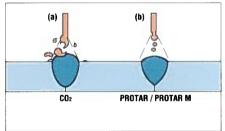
Efecto de la composición del gas sobre la transferencia del metal de aportación en la Soldadura MIG-MAG "Arco Spray"
